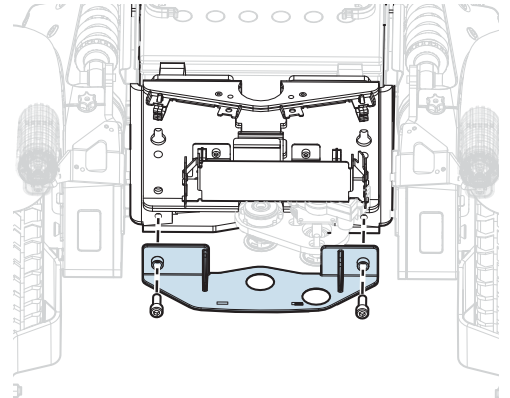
Entfernen Sie die Schutzplatte unter dem Motor.
